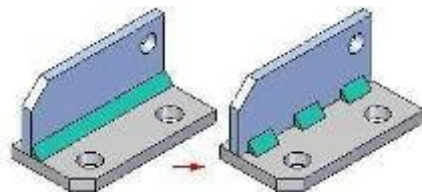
Cordones de soldadura creados en el entorno de soldadura (Solid Edge V17 ©).
